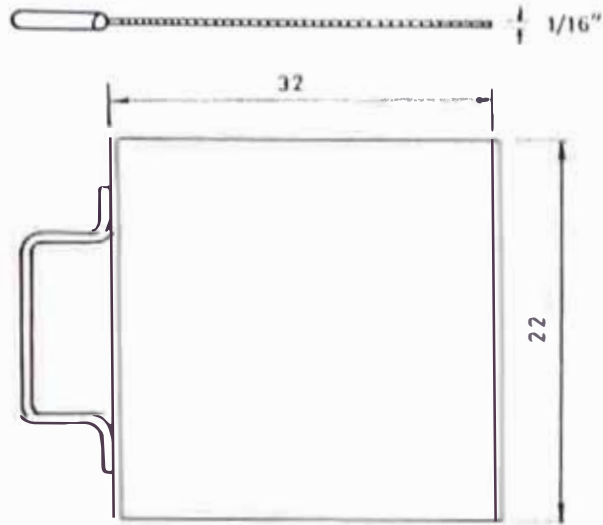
PLANCHA DE CONSTRUCCION DE LA VALVULA DE DESCARGA
